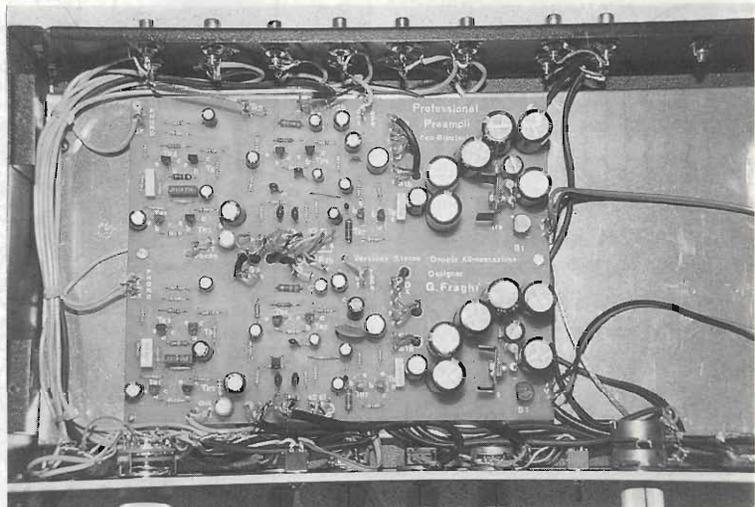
Vista interna con primo piano della scheda madre montata e cablata.
